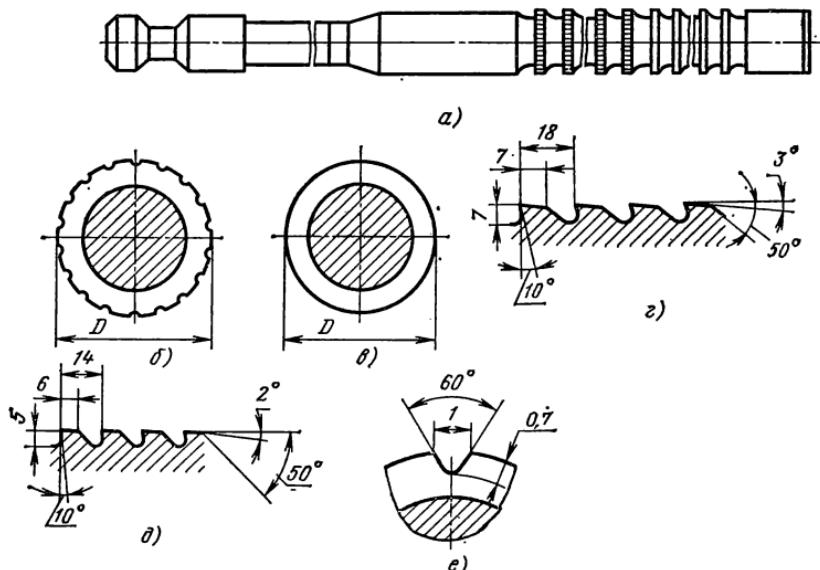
Круглая протяжка с профильной схемой резания зубьев:
